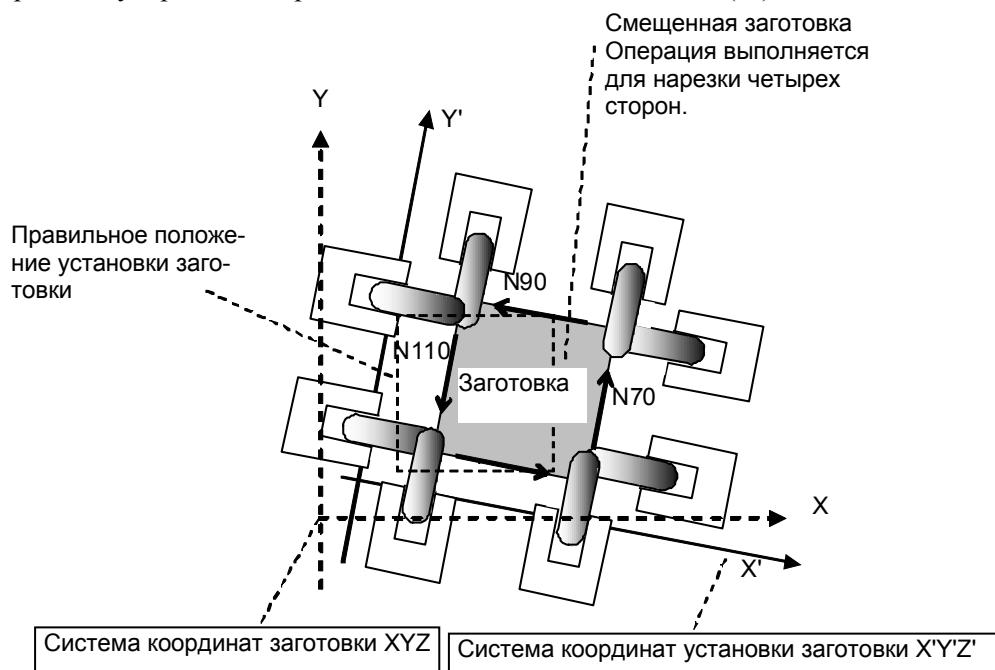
(aa) Операция управления центром инструмента при наличии погрешности установки заготовки
